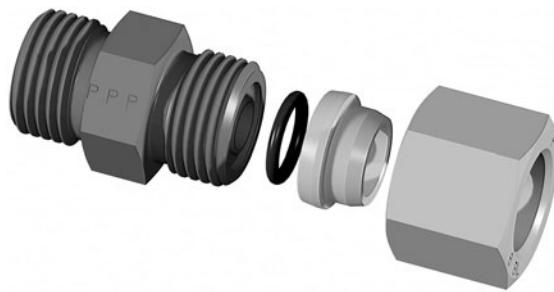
Cuerpo de la Conexión Seal-Lok, O-ring, Barril y Tuerca
